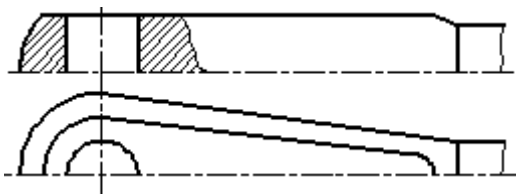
Образец оформления линий пересечения поверхностей.
